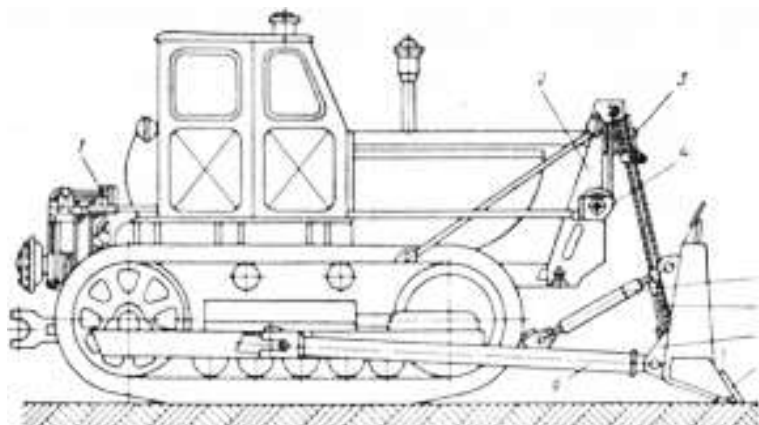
Бульдозер ДЗ-53 с неповоротным отвалом и с канатным приводом: 1 — приводная лебедка; 2 передняя стойка; 3 неподвижная обойма полиспаста; 4 — направляющий блок; 5 — винтовые раскосы; 6 — подвижная обойма полиспаста; 7 — отвал; 8 — ножи; 9 — толкающие брусья
